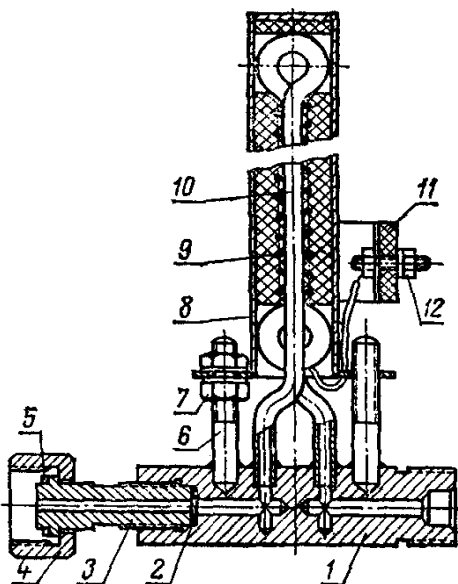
Подогреватель углекислого газа: 1 – штуцер; 2 и 5 – прокладки; 3 – патрубок; 4 – накидная гайка; 6 – стойка; 7 – гайка; 8 – кожух; 9 – нагревательный элемент; 10 – змеевик; 11 – панель; 12 – зажим подогревателя
